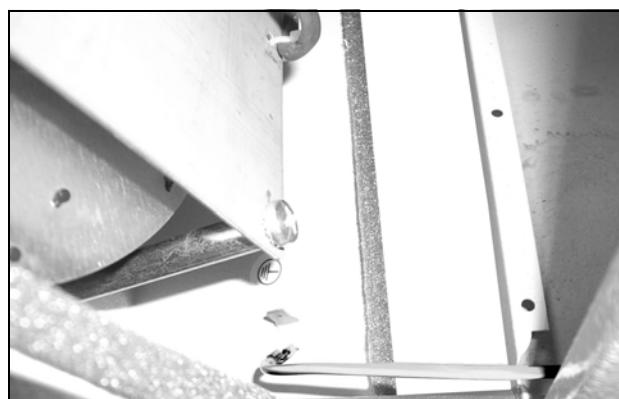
Provléknutí kabelu displeje kabelovou průchodkou
